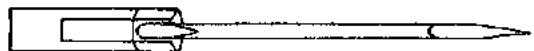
Soldador de filo (Electric Materials Co.)
